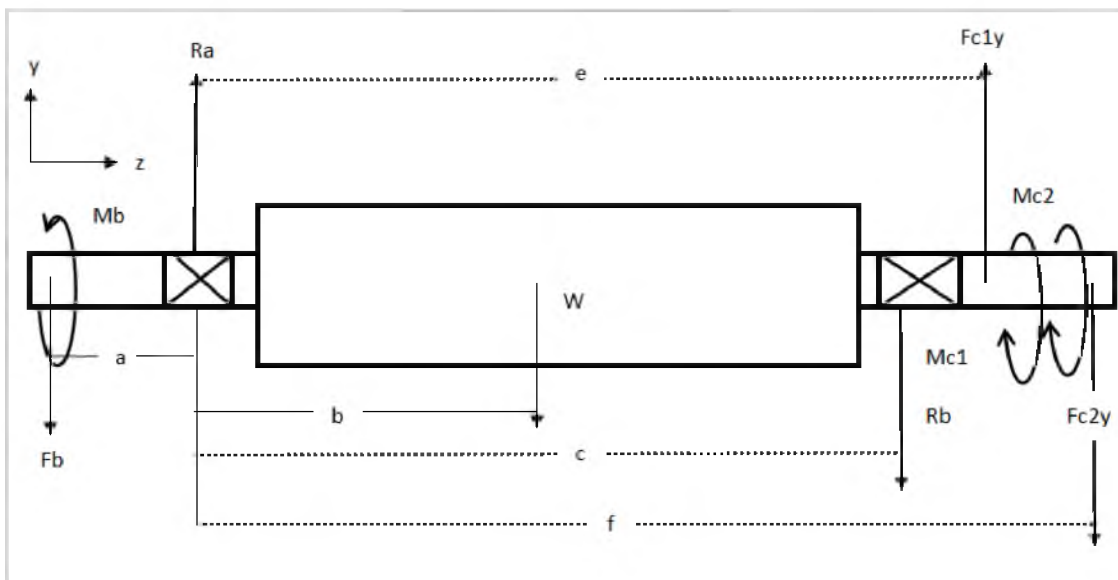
Cargas en el plano yz del cilindro desfibrador
